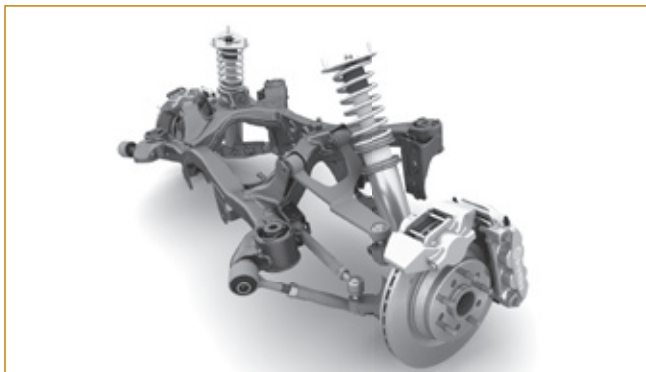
Подвеска в сборе. Фотореализм в T-FLEX CAD
